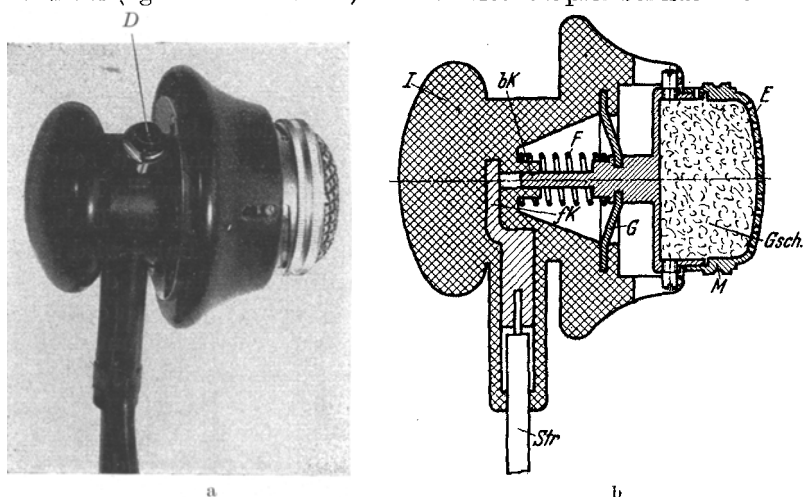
Bei a mobile Elektrode in Seitenansicht; bei b mobile Elektrode auf dem Längsschnitt (Werkzeichnung von Siemens-Reiniger). Für die Schnittzeichnung gilt: E Elektrodenfläche, Gsch Gummischwamm, M Metall, G Gummidichtung, F Feder, δK beweglicher Kontakt, I Isolation, fK fester Kontakt, Str Stromzuführung. Die Rückmeldeeinrichtung ist im Schnitt nicht eingezeichnet. Der Druckknopfkontakt der Rückmeldeeinrichtung ist bei Seitenansicht (D) kenntlich.
